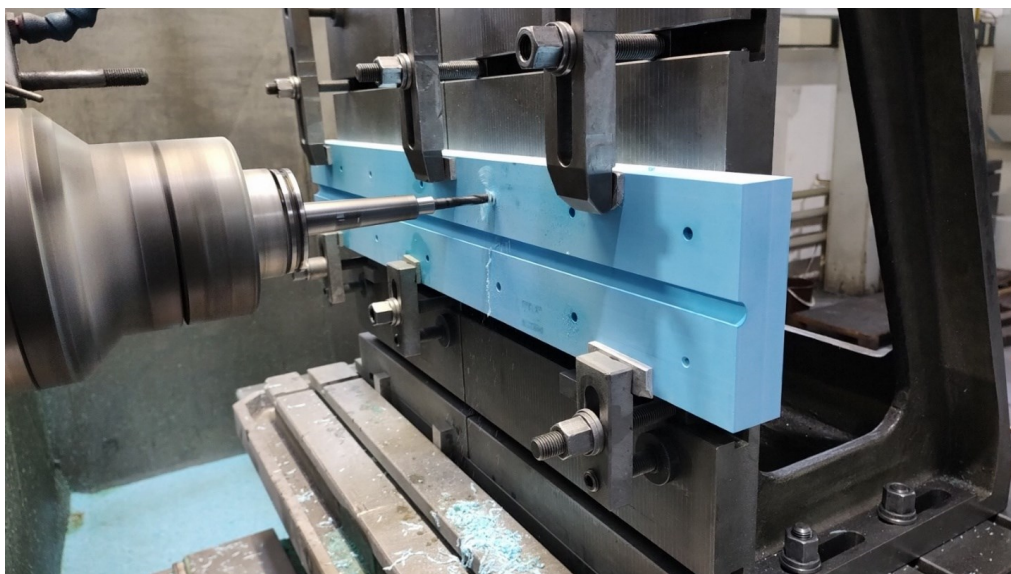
Obrobený bok upnutého bloku na CNC frézovacím stroji
